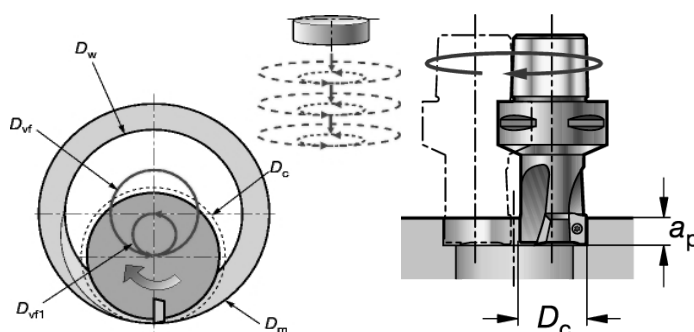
Круговая интерполяция с врезанием по 2 осям: а- схема врезания фрезы 1 вдоль оси заготовки 2 методом винтовой интерполяции заготовки; D_w – диаметр отверстия обрабатываемой заготовки; D_{vf} – траектория оси шпинделя с фрезой в начале врезания фрезы; D_{vf1} – траектория оси шпинделя с фрезой в конце врезания фрезы; D_m – диаметр окончательно обработанной поверхности; б – схема врезания фрезы перпендикулярно оси заготовки, a_p – величина подачи фрезы за 1 оборот заготовки или планетарного поворота борштанги с фрезой вокруг оси отверстия (рекомендации фирмы Sandvik).
